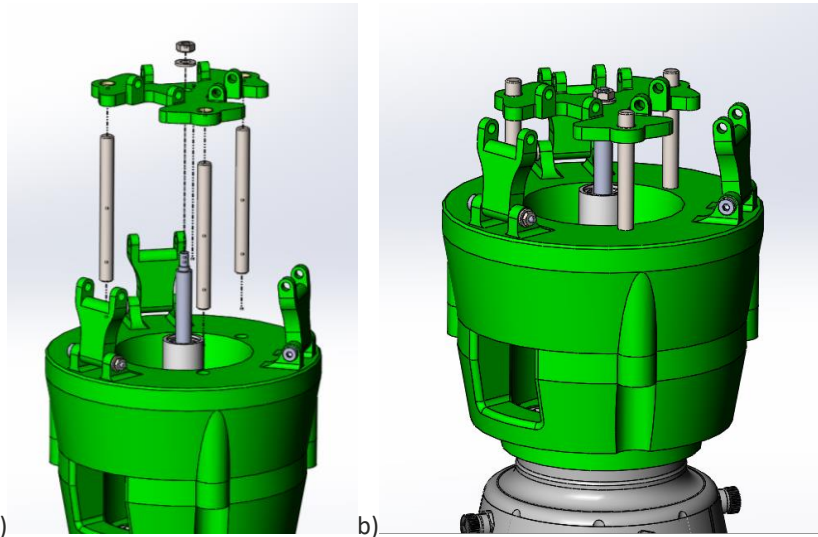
6ª parte da montagem - vista explodida da montagem (a) e parte da montagem completa (b).
